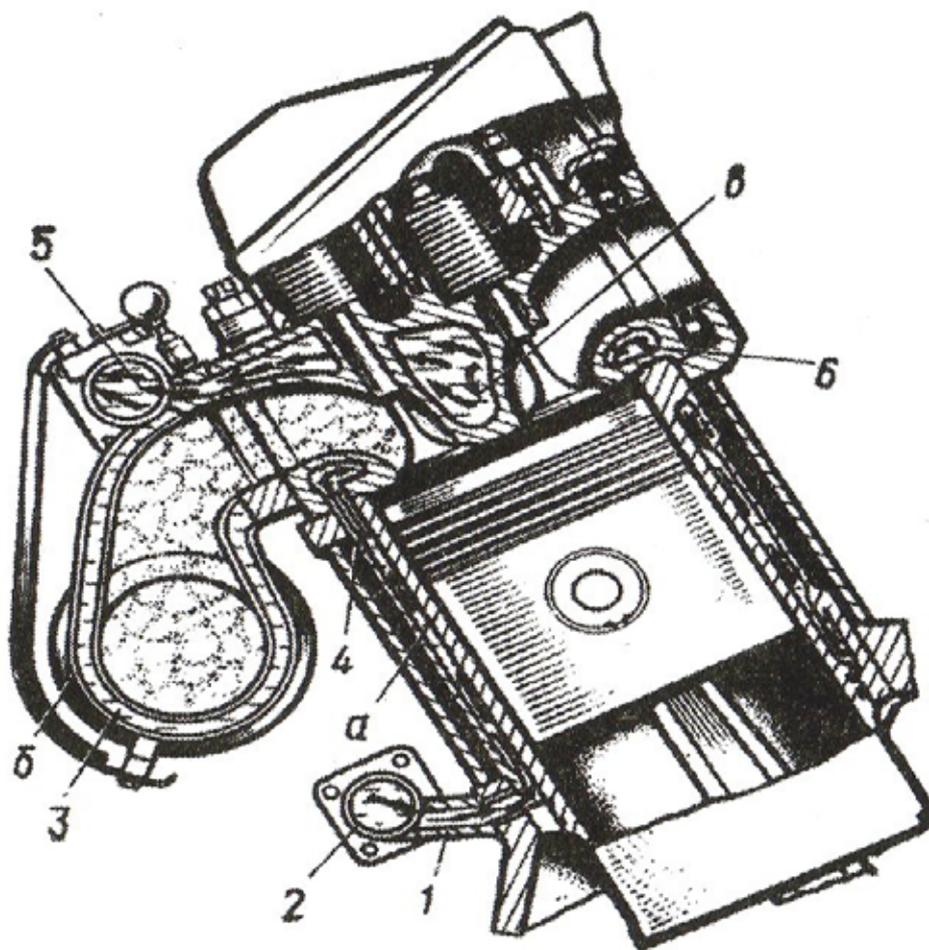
Схема охлаждения цилиндра и крышки дизеля 2А-5Д49:
